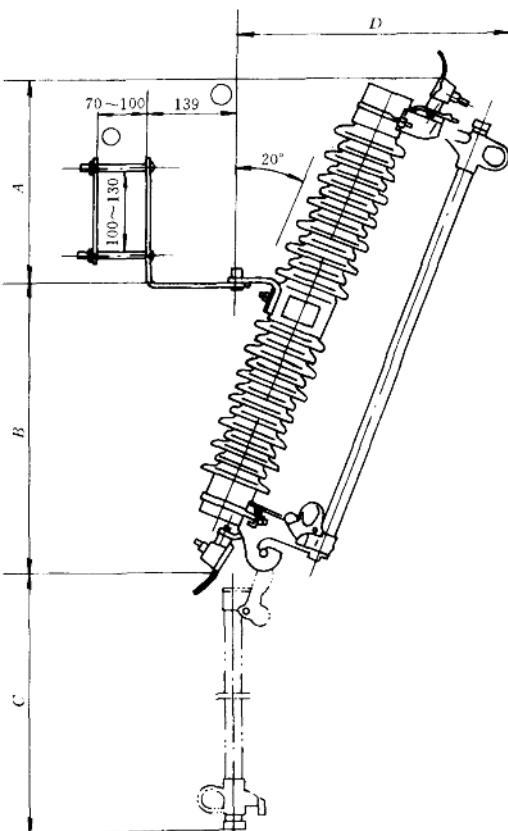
PRWG₂ 型跌落熔断器外形尺寸
